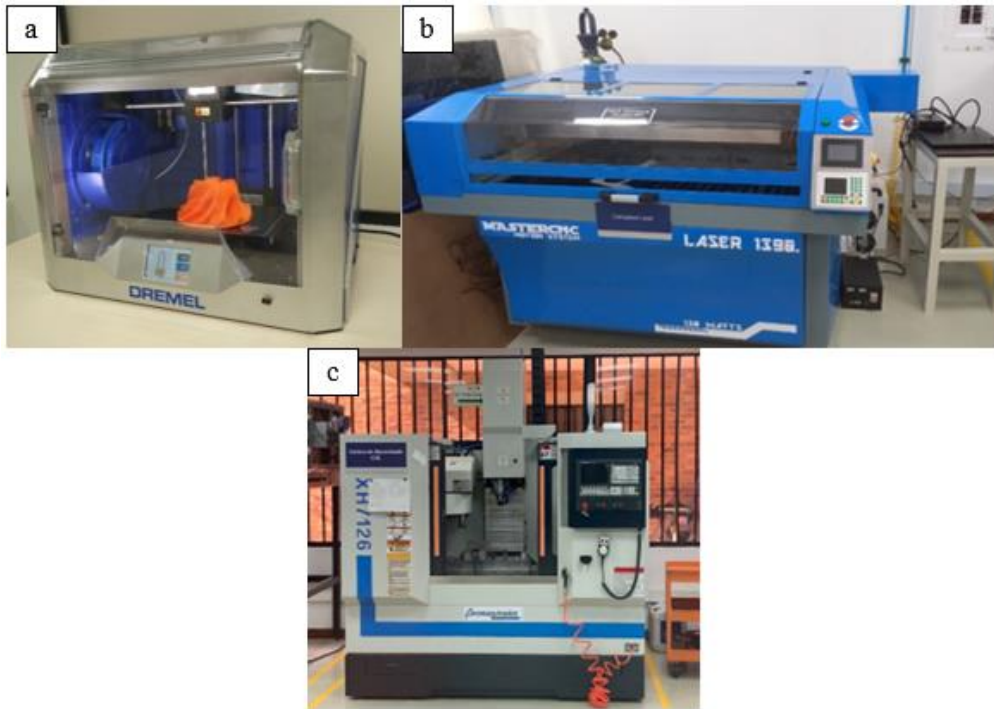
Máquinas para prototipado. a) Impresora 3D Dremel 3D40, b) Cortadora láser Mastercnc laser 1390, c) Centro de mecanizado CNC
